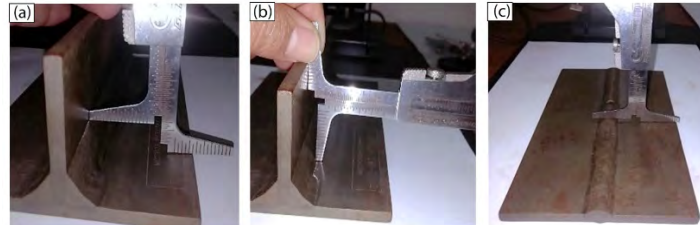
Disposición de Hi-Lo Gauge para dimensionar el tamaño de (a, b) ambas piernas en soldadura de filete y (c) refuerzo en junta a tope
